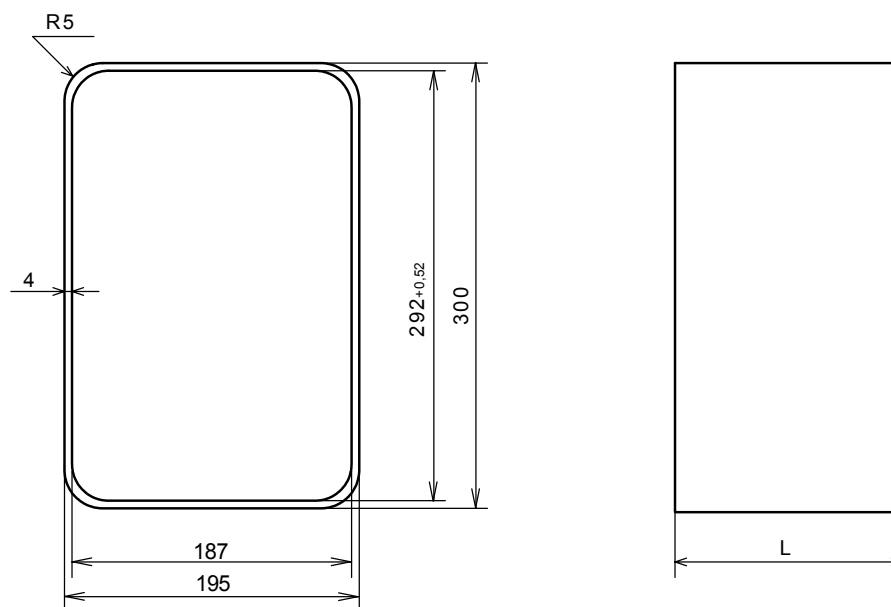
Габаритные, присоединительные и установочные размеры блока
